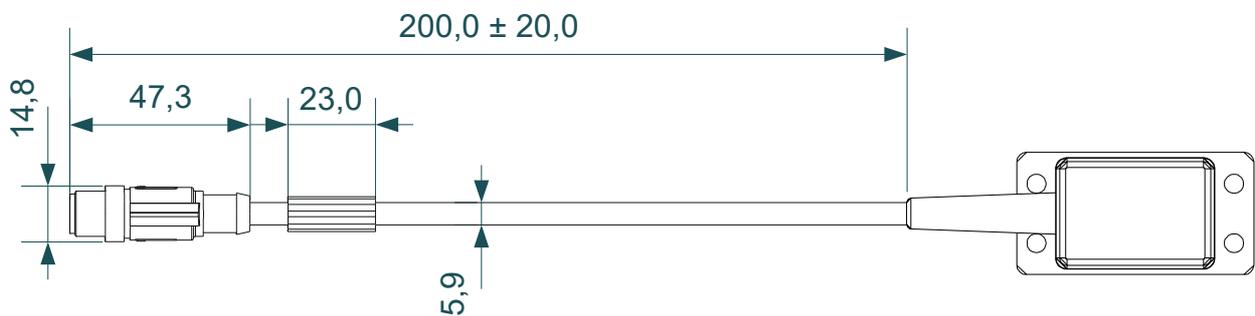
Maßzeichnung Anschlusskabel (Maße in mm)
